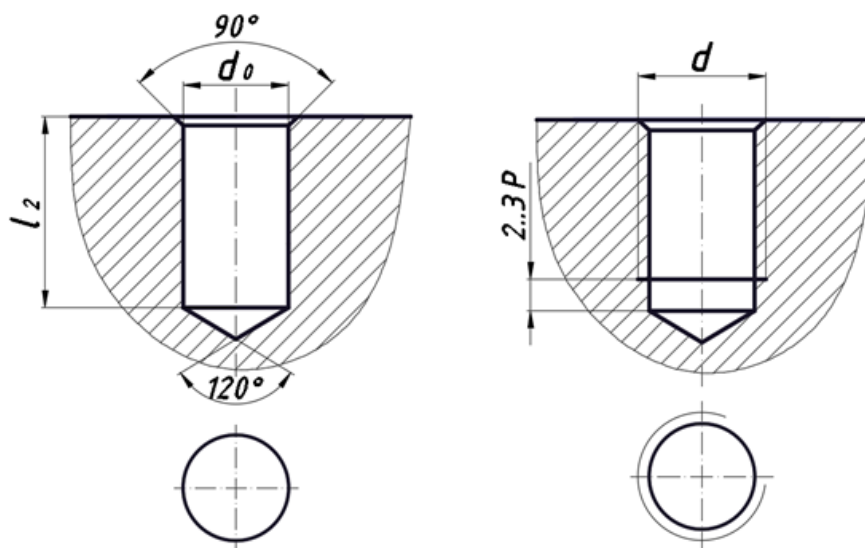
Образец оформления глухих резьбовых отверстий под винты
